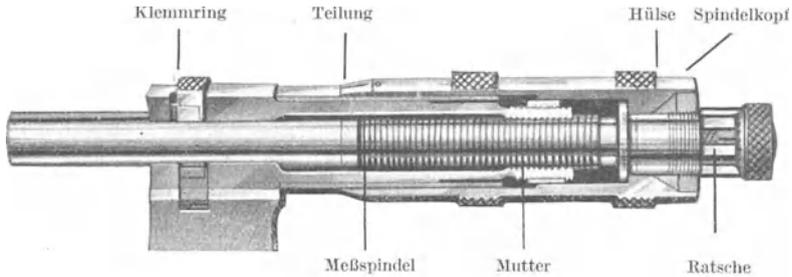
Spindel und Mutter der Schraublehre von Carl Zeiß, Jena.
